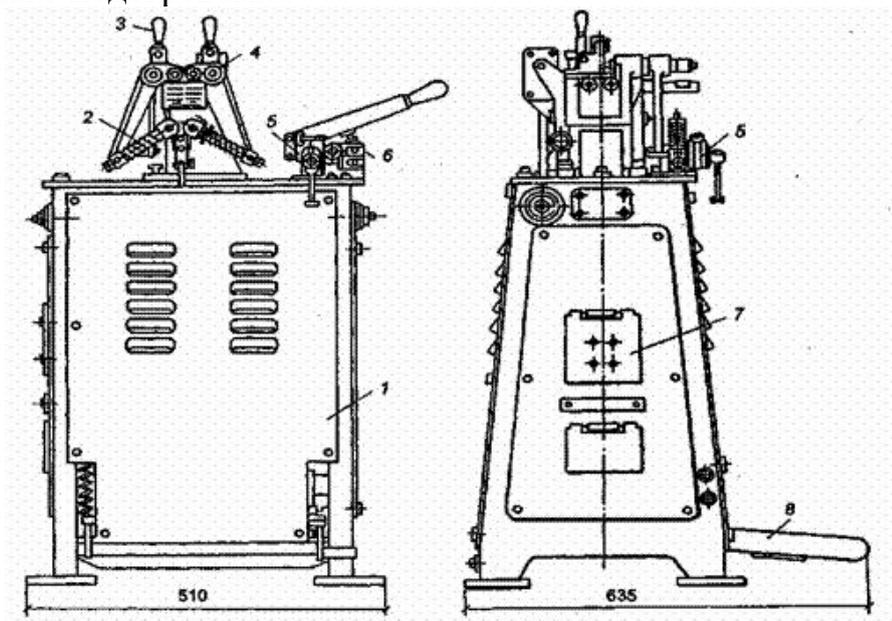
Машина МС – 502 для стыковой сварки:
